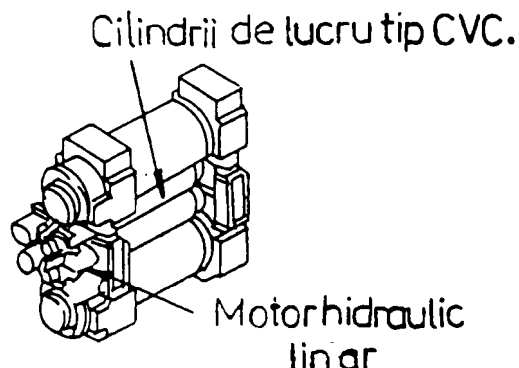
Ansamblul echipat cu cilindri rectificați în formă de S
